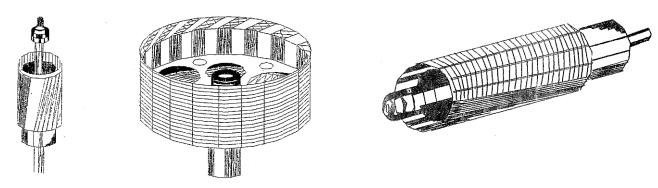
Diferentes rotores de un motor de bobina móvil.
